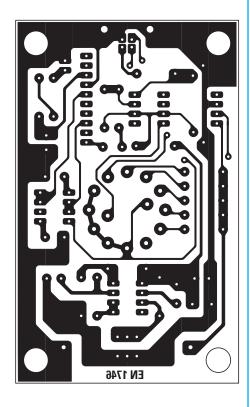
Dessin à l'echelle $\mathbf{1}$, du circuit imprimé EN1746 vue côté soudure
